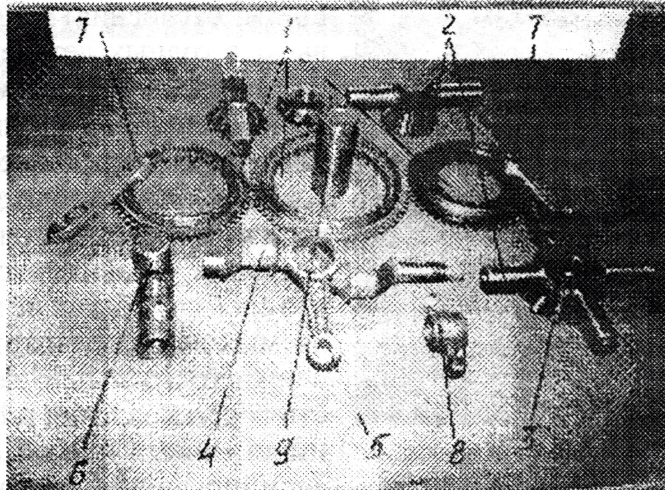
Зубчатые синхронизаторы – 1, крестовина и ось крестовины дифференциала – 2, шестерня коническая дифференциала – 3, вал коленчатый компрессора – 4, шатун компрессора – 5, толкатель клапана – 6, рычаги (лапки) сцепления – 7, коромысло – 8, палец поршневой – 9
